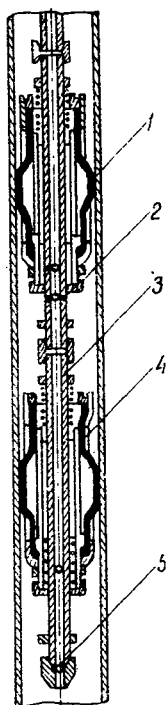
Двойной шаговый пакер (рабочее положение): 1—эластичный баллон; 2—отверстия; 3—штанга; 4—цанга; 5—обратный клапан.
